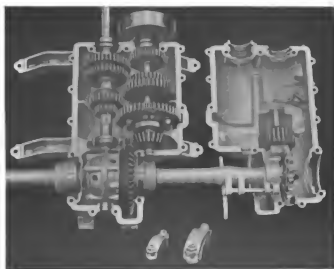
Getriebe-Kasten für Fahrzeug IV und V.
